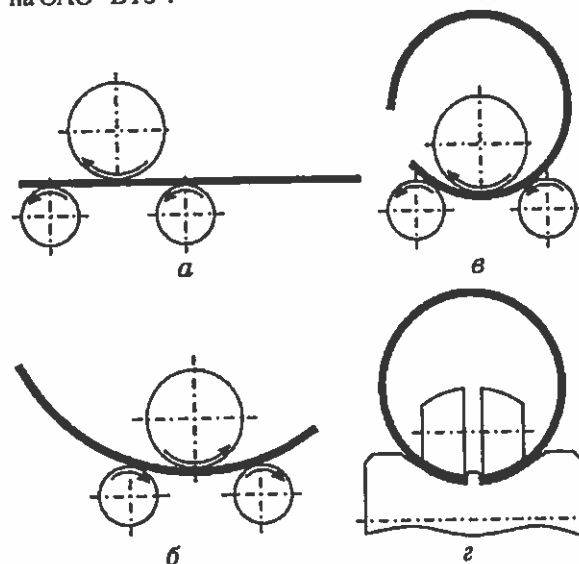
Основные операции формоизменения трубной заготовки при производстве прямошовных сварных труб большого диаметра: а – в – формовка на вальцах в один или несколько проходов; г – формовка прикромочной зоны в роликовой кассете.
